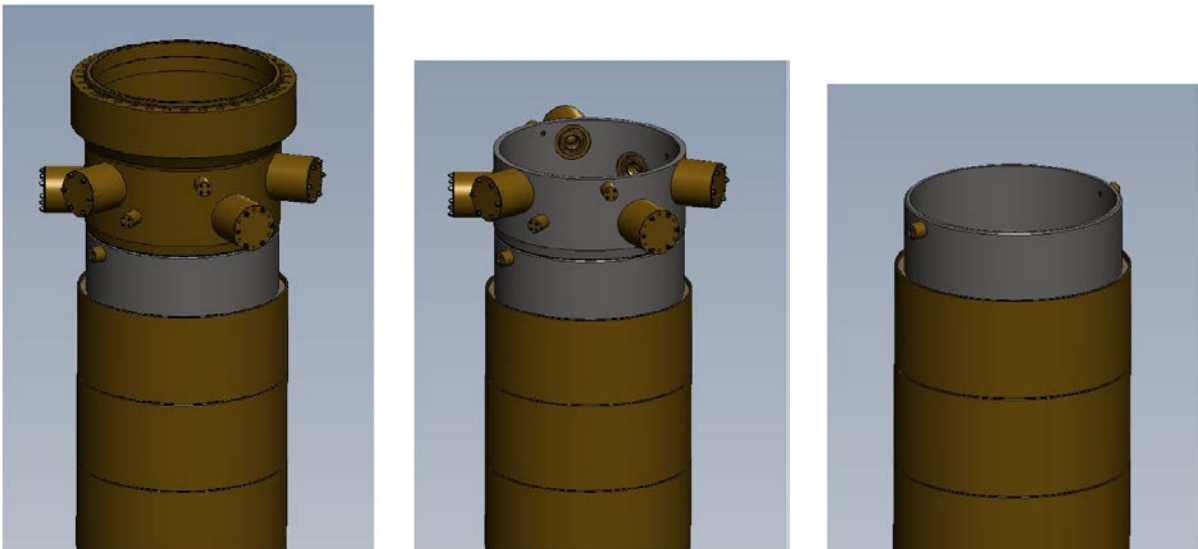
Schussweise Zerlegung des RDB im Betonschacht
